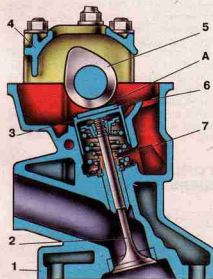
Механизм привода клапанов: 1 – головка цилиндров; 2 – клапан; 3 – толкатель; 4 – корпус подшипников распределительного вала; 5 – распределительный вал; 6 – регулировочная шайба; 7 – маслоотражательный колпачок; А – зазор между кулачком и регулировочной шайбой
